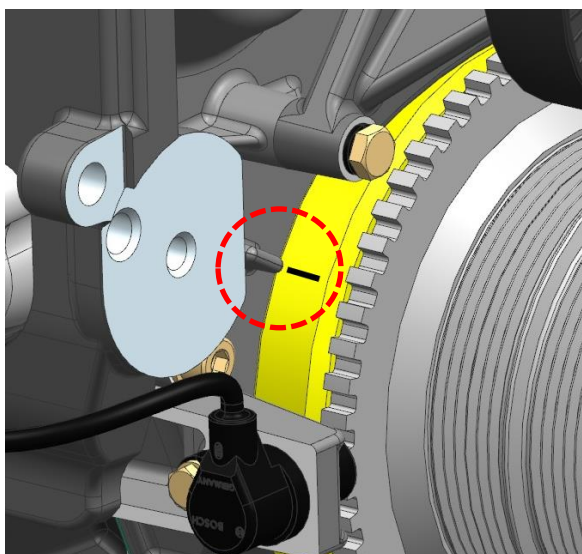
Риска на шкиве коленчатого вала и указатель на крышке цепи
